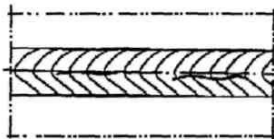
9. Продольные трещины сварного соединения
